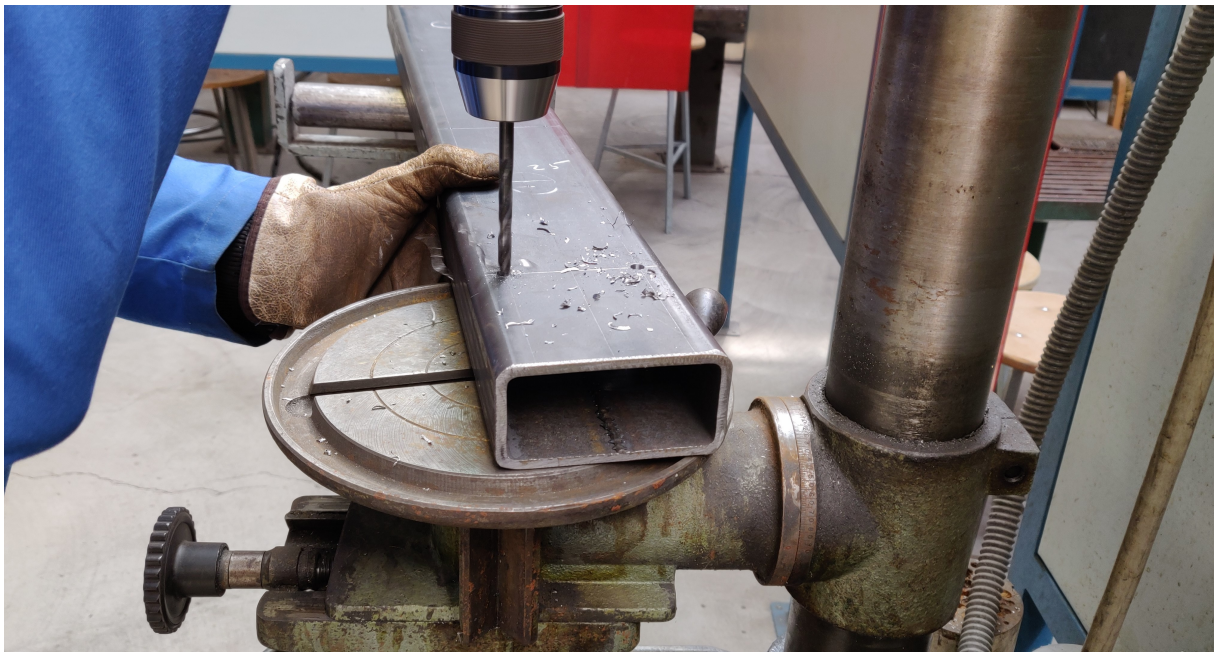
Mecanizado de los pilares mediante la taladradora en columna.
